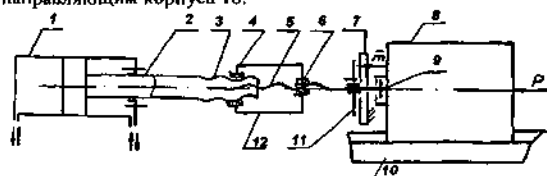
Схема привода, позволяющая разгрузить привод подачи и повысить точность обработки
